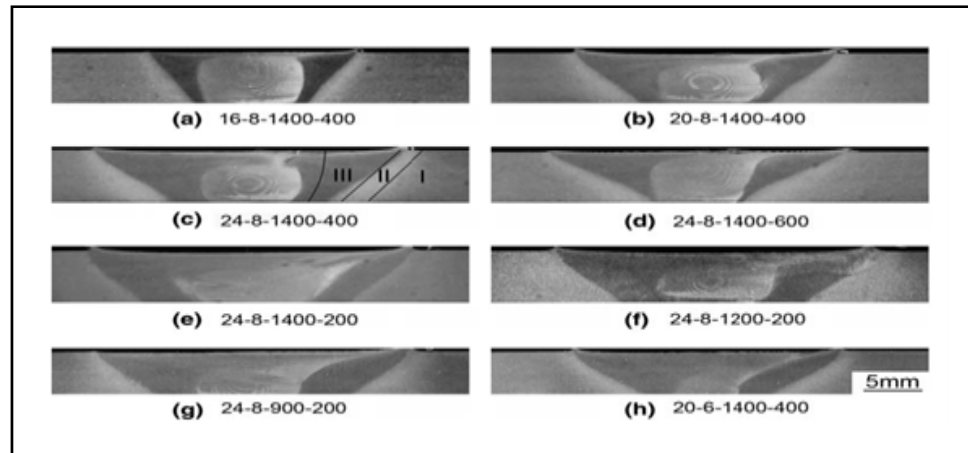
Macrographies de coupes transversales de soudure par friction-malaxage d'un AA 6061-T651 (Liu and Ma 2008)
